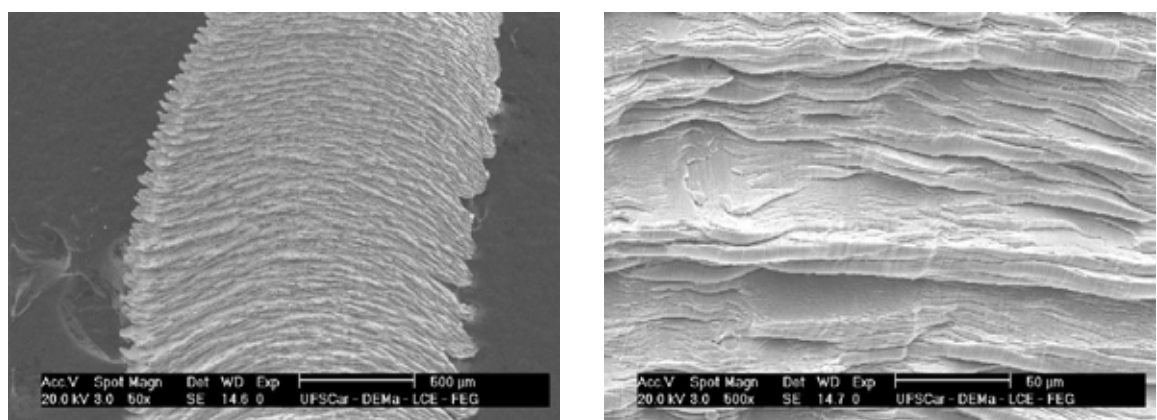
Cavaco extraído da amostra (F) sob a condição de usinagem C3.
